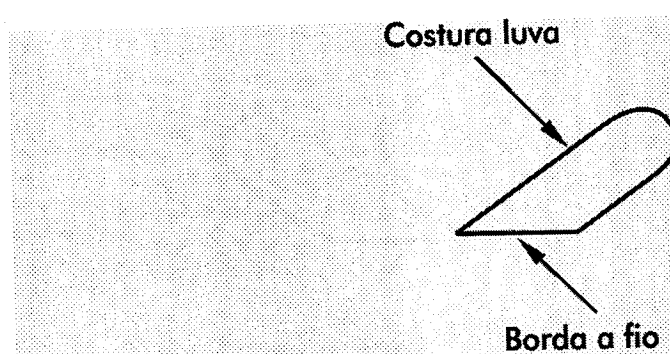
Desenho técnico da peça 3 do meio do 3º e 4º dedo
